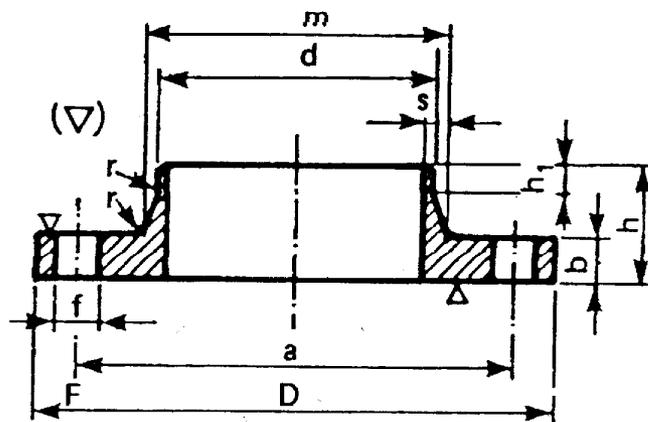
Flangia a collare per tubazioni da saldare di testa.
